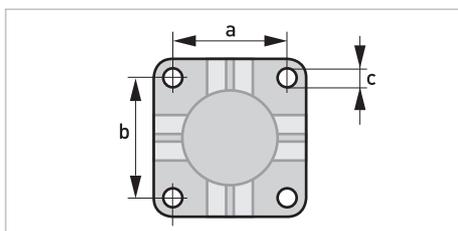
Dimensions pour plaque de montage du boîtier intempéries
